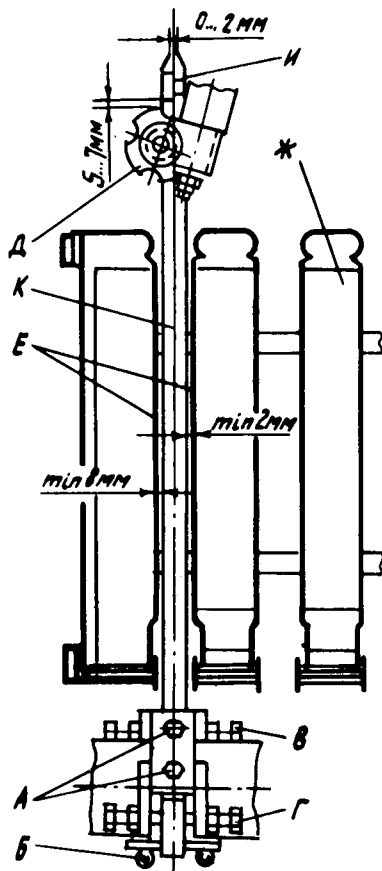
Регулировка установки игол относительно поршня и диска зажима
